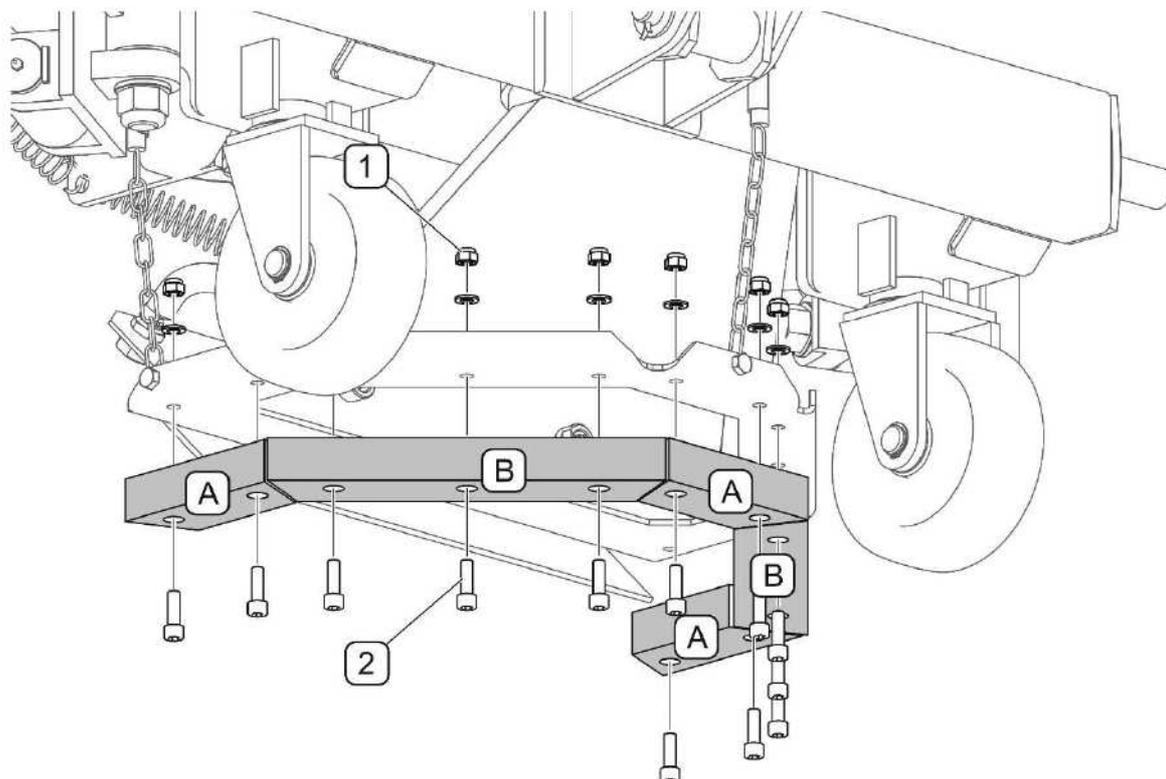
Le remplacement des glissières de l'embout aspirant
